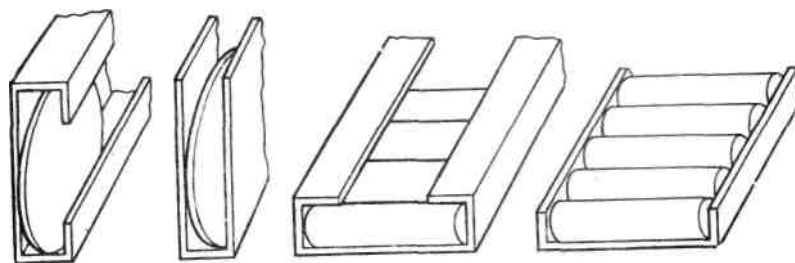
Лотки-скати для транспортування заготовок типу валів і дисків
